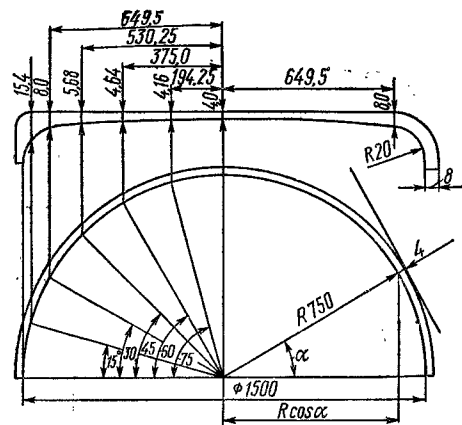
Способ и пример расчета сечения заготовки для изготовления сферической оболочки
